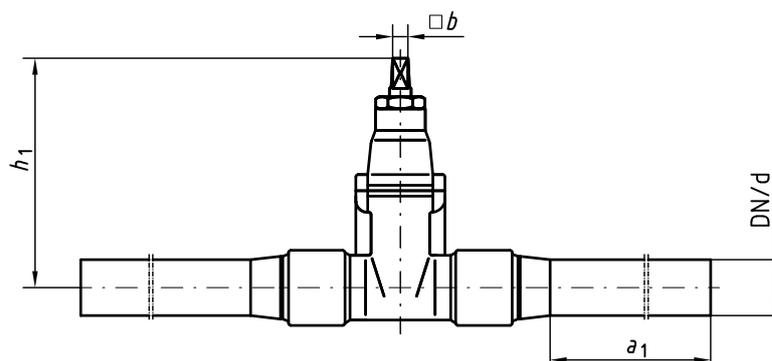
Hausanschlusschieber mit Einschweißenden aus PE
